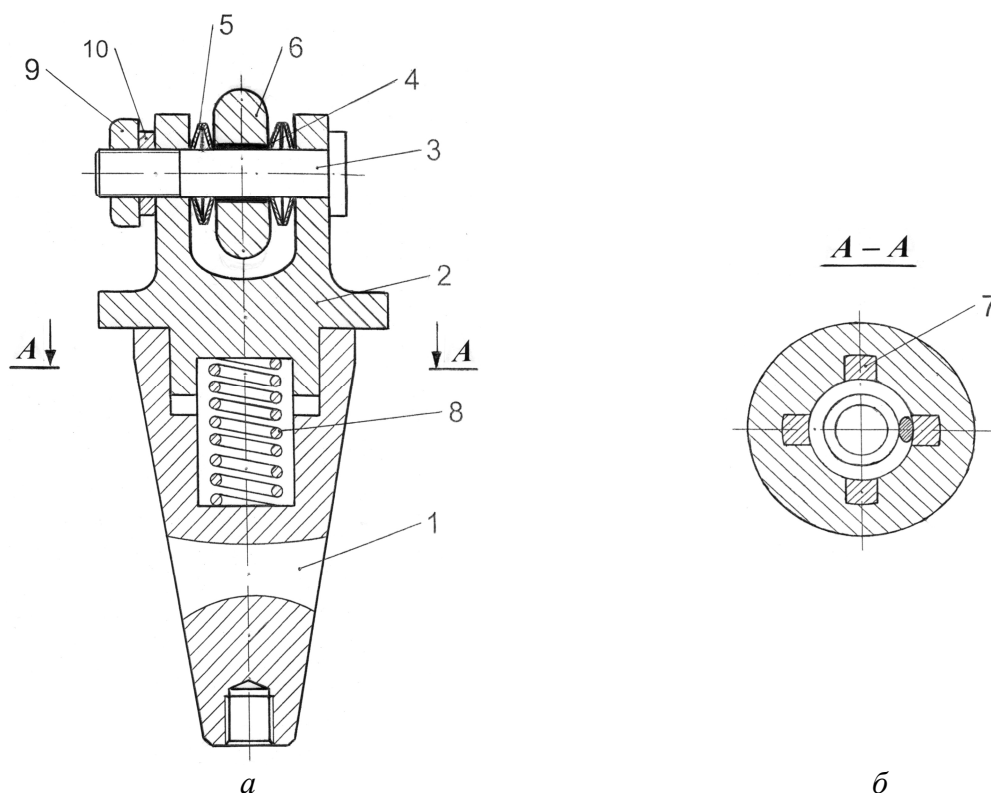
Устройство для упрочняющей обработки плоских поверхностей деталей
